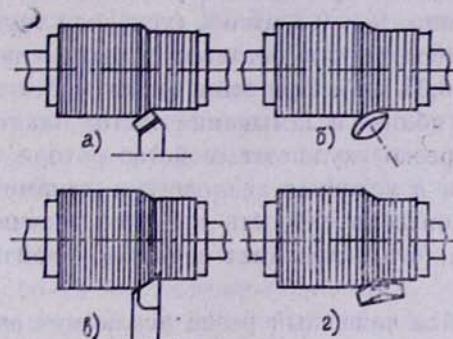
Схемы обточки роторных сердечников различными инструментами:
